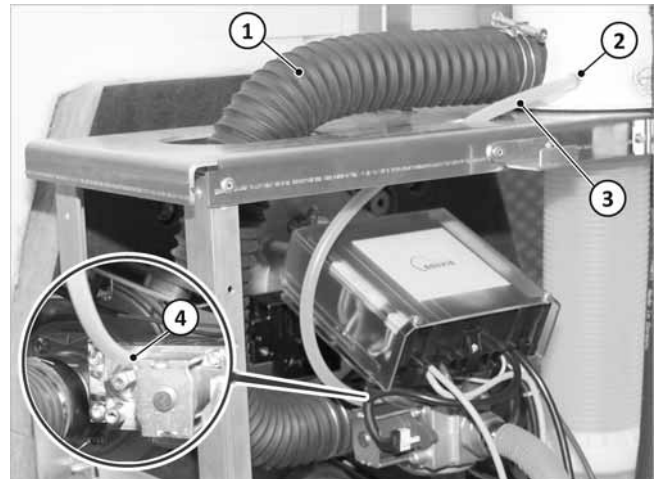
Zuluft- und Druckausgleich-Schlauch aufstecken
